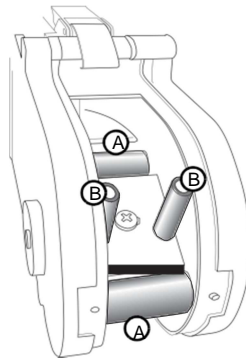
Galets (A) et rails (B) sur le rotor de la pompe
